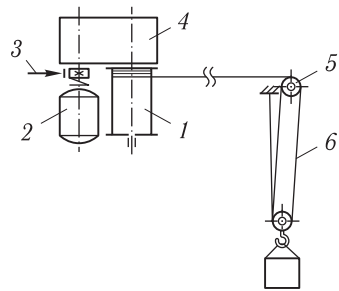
Кінематична схема підйомного механізму: 1 — канатний барабан; 2 — електродвигун; 3 — гальмо; 4 — редуктор; 5 — нерухомий блок; 6 — поліспаст
